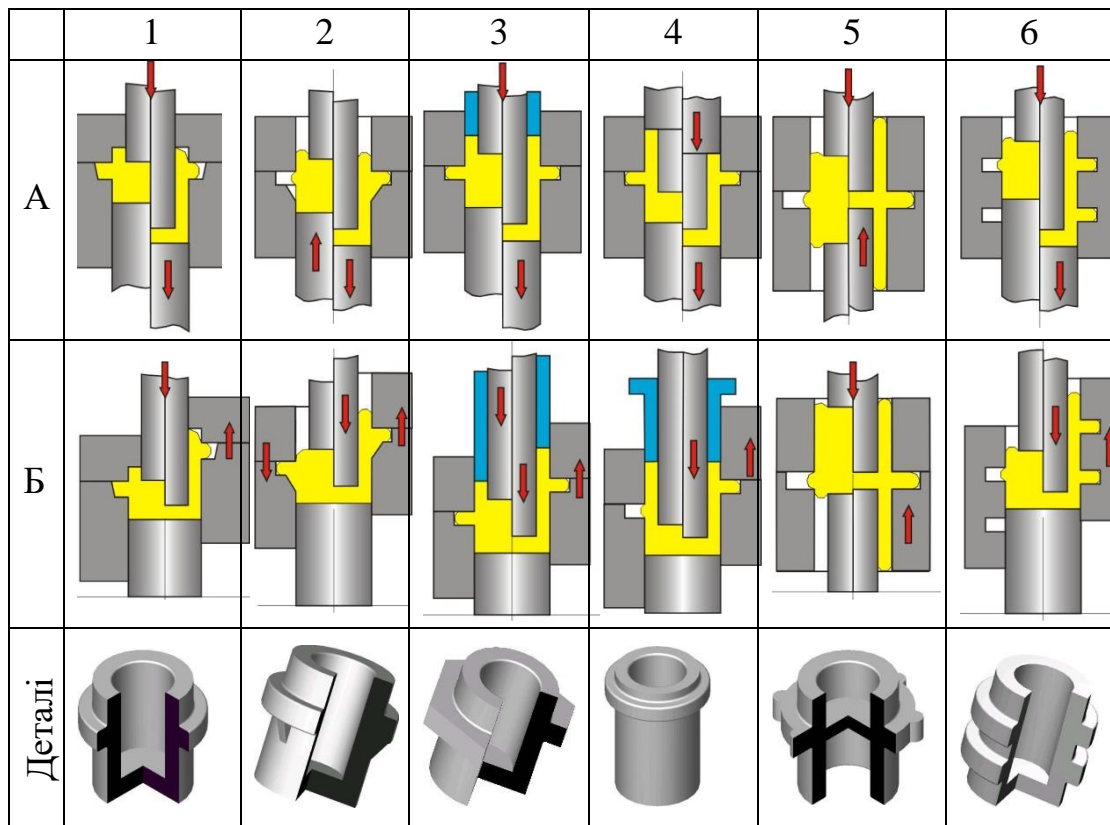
Способи поетапного комбінованого видавлювання
